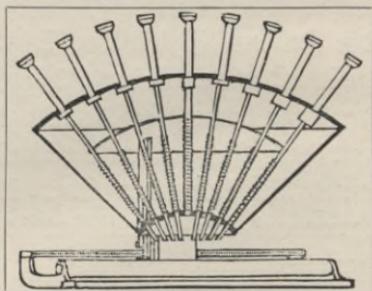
Mechanismus von Schades Typenstabschreibmaschine.
